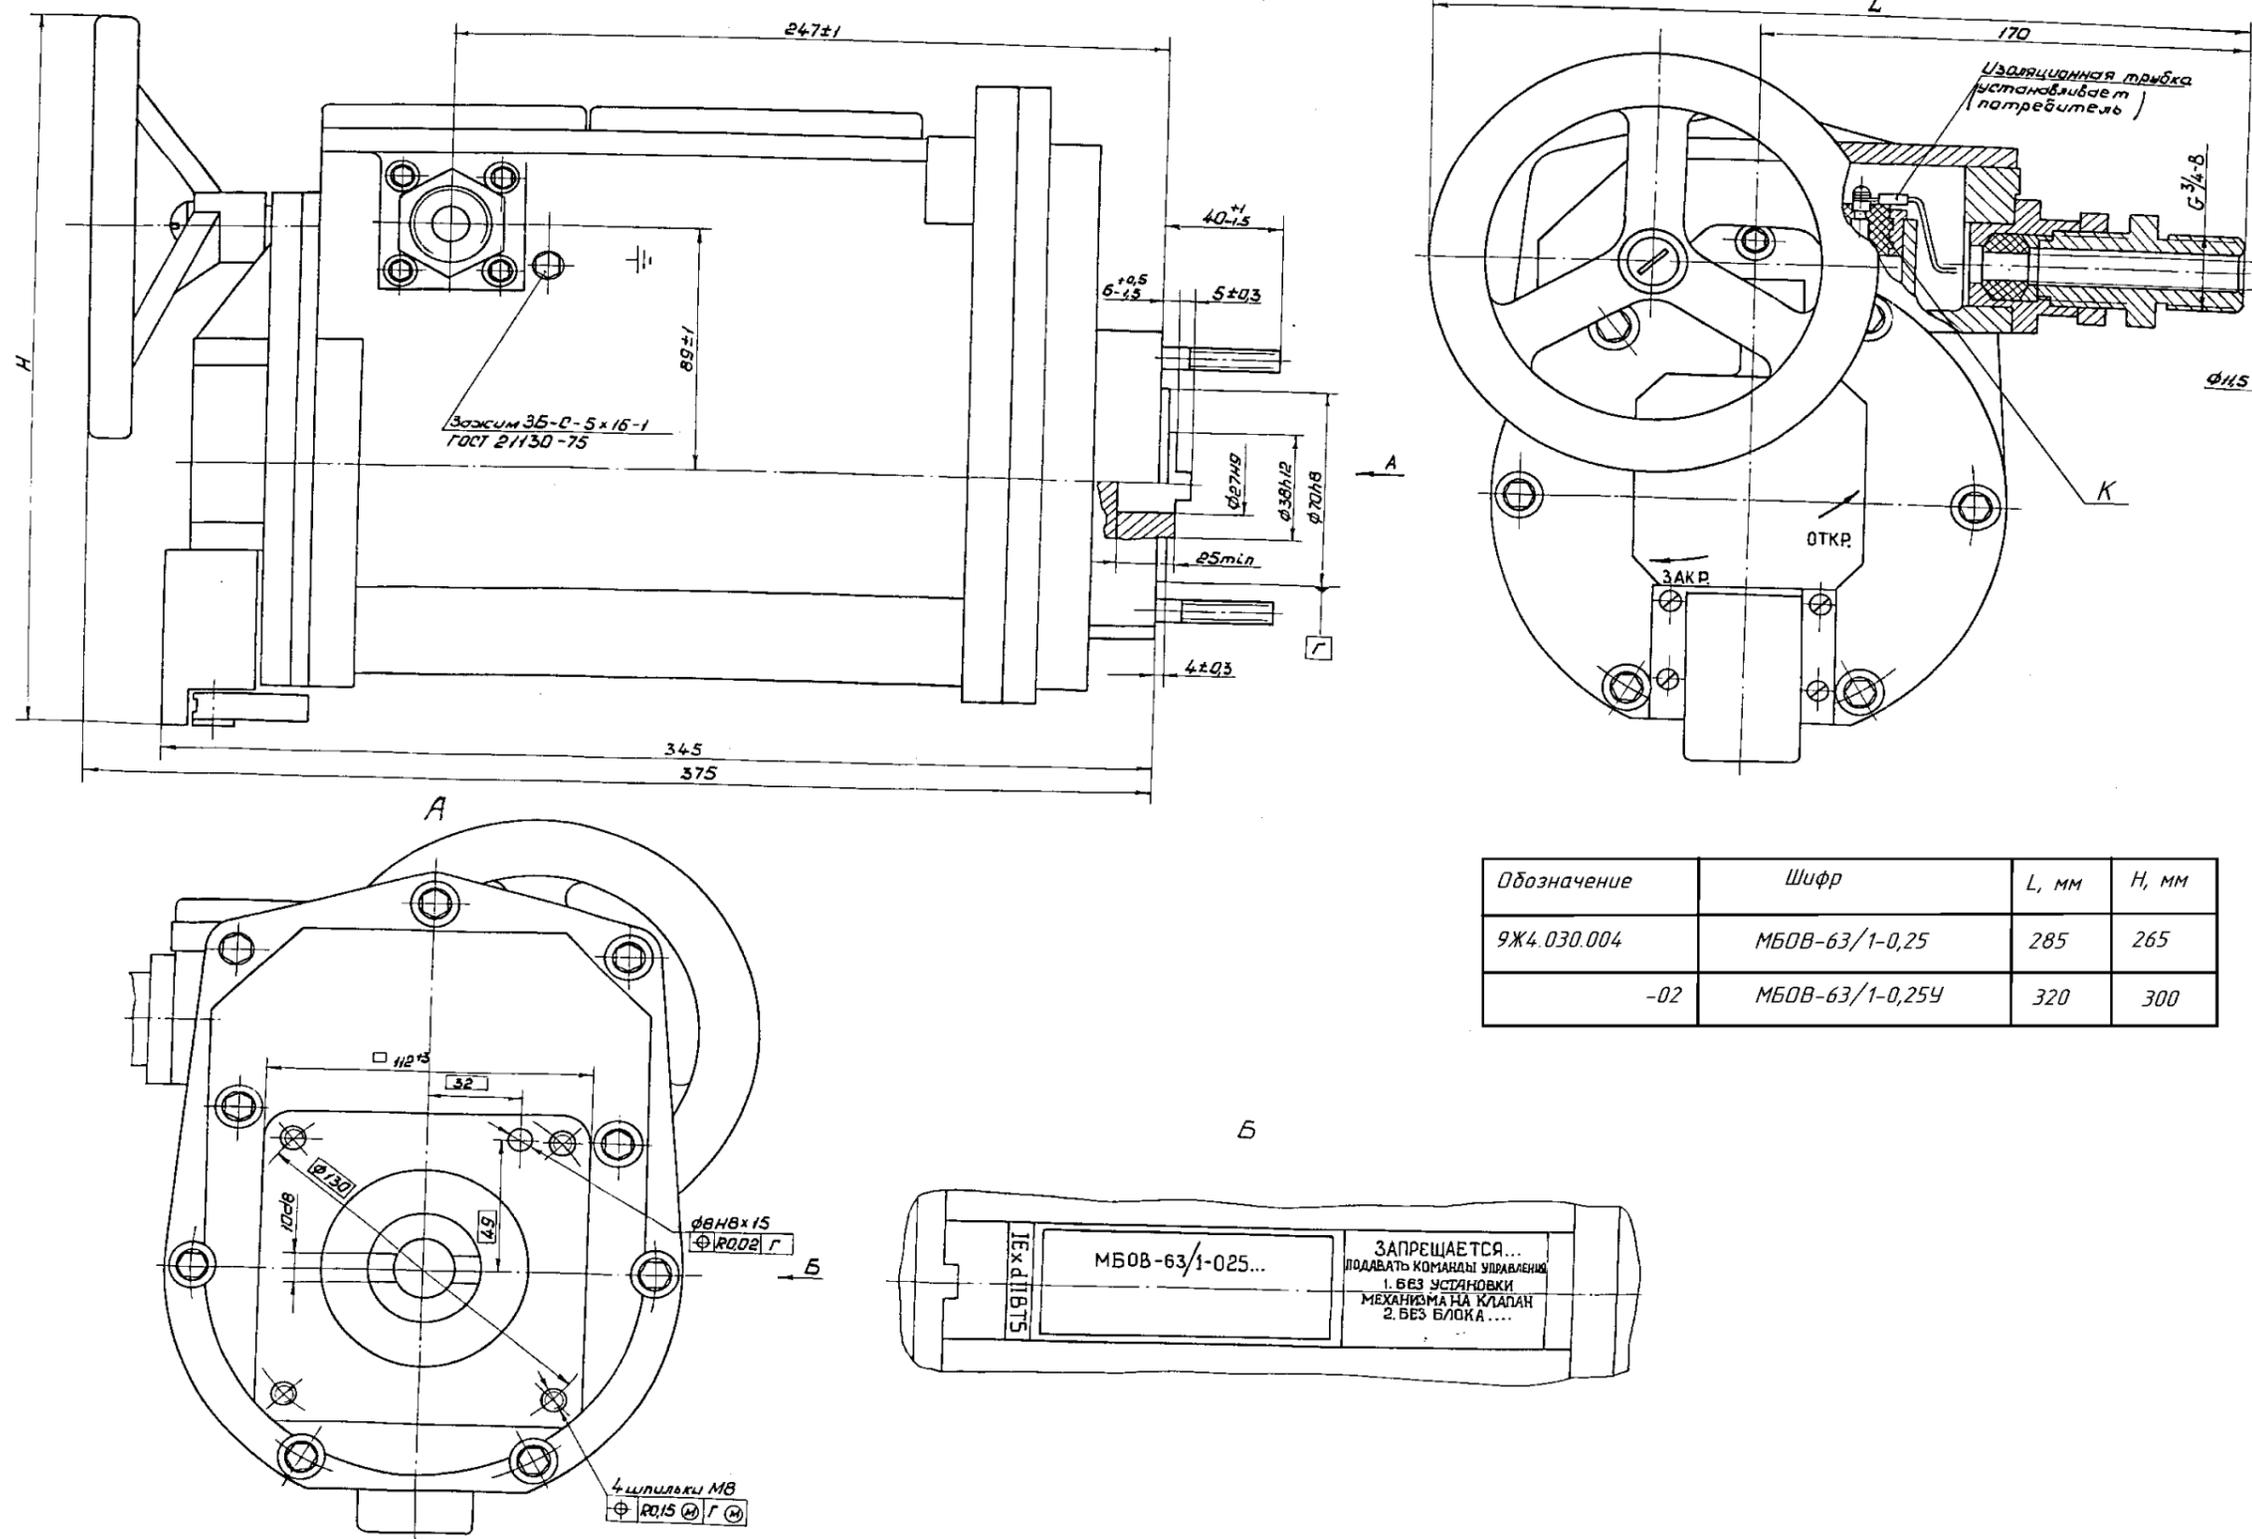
Габаритный чертеж электропривода МБОВ-(40-125)
